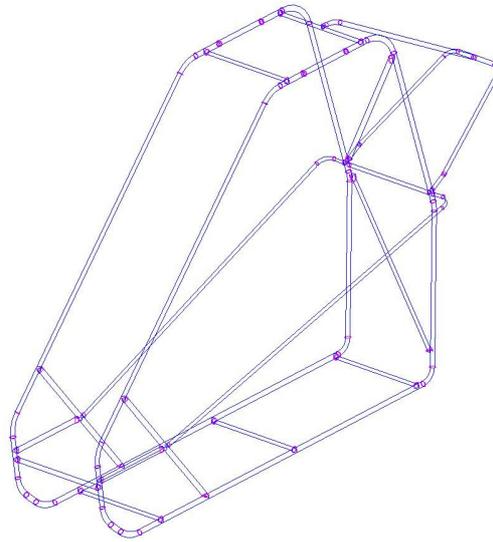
Modelo idealizado pro Midsurfaces e End Welds
